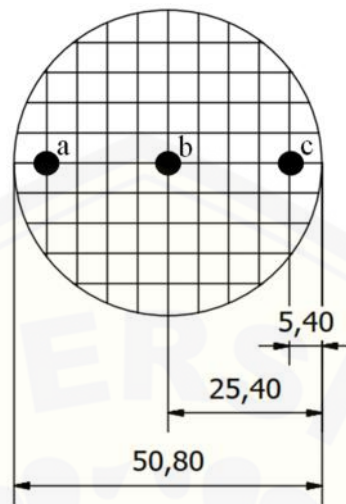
Benda kerja setelah proses *milling* CNC
